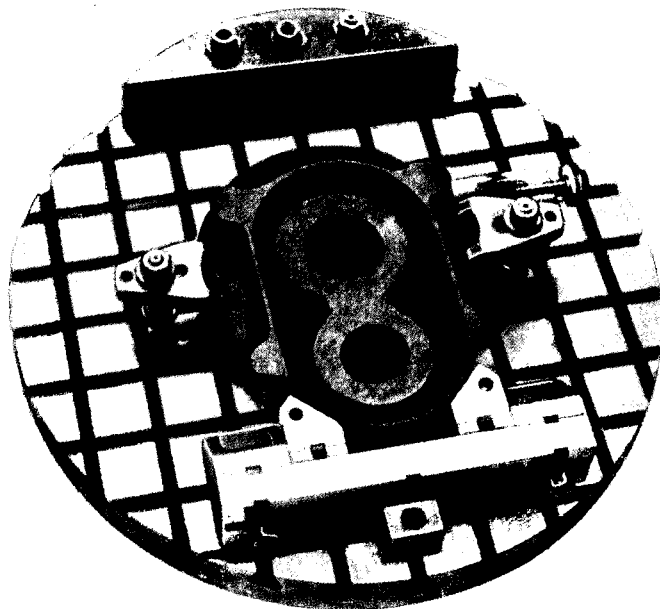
Токарное приспособление для расточки отверстия в корпусе крышки
